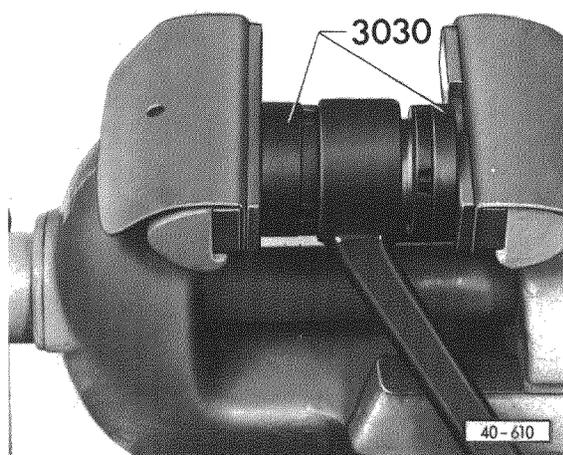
Gummimetallager für Querlenker zwischen Schraubstockbacken einpressen
